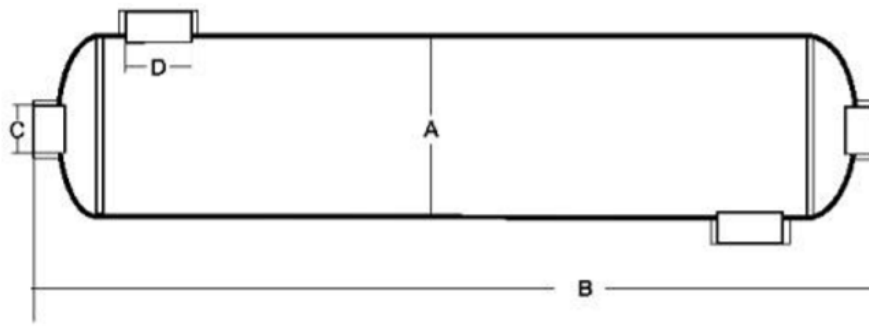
14. Dimensiones principales del intercambiador de tubo y carcasa. Fuente: [24].
